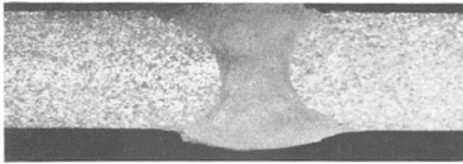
Aluminiumblechschweißung, Schweißdraht mit Titanzusatz, Rohschweiße.
